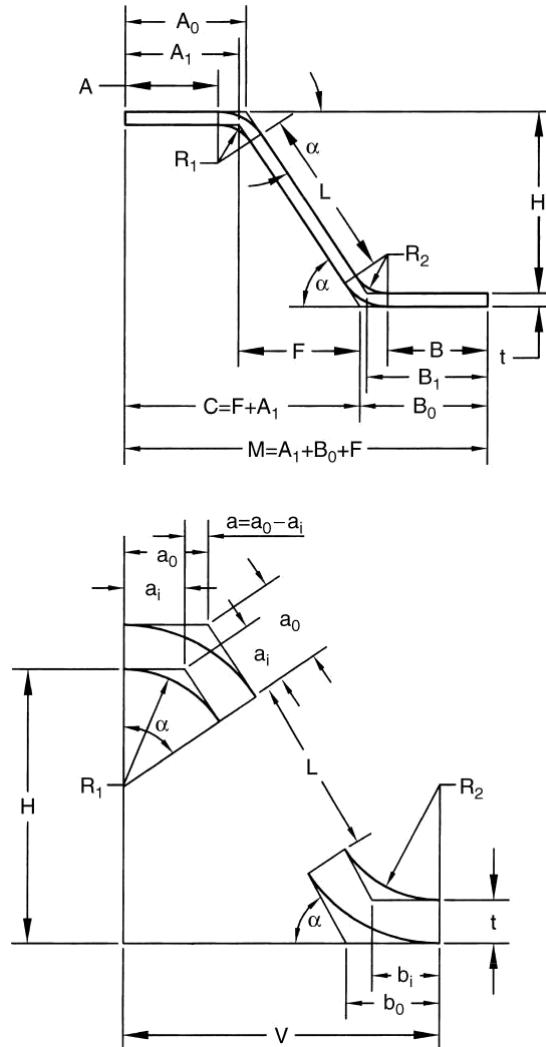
Схематичне зображення криволінійної ділянки заготовки
